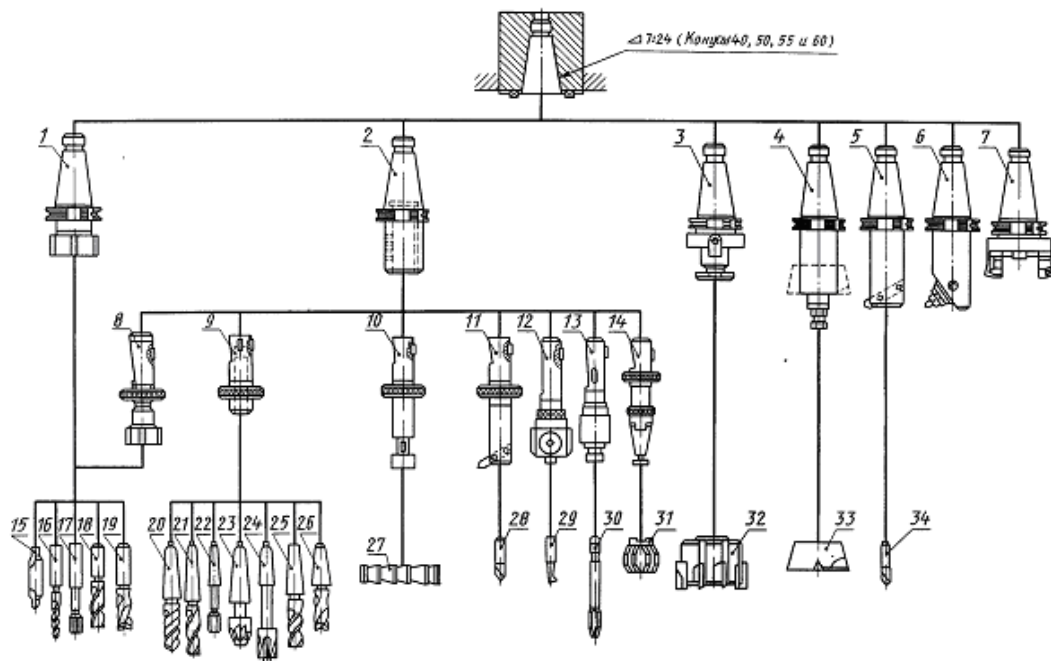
Типовий технологічний комплект для багатоцільових свердлильно – фрезерно-розточувальних верстатів зі ЧПК.
